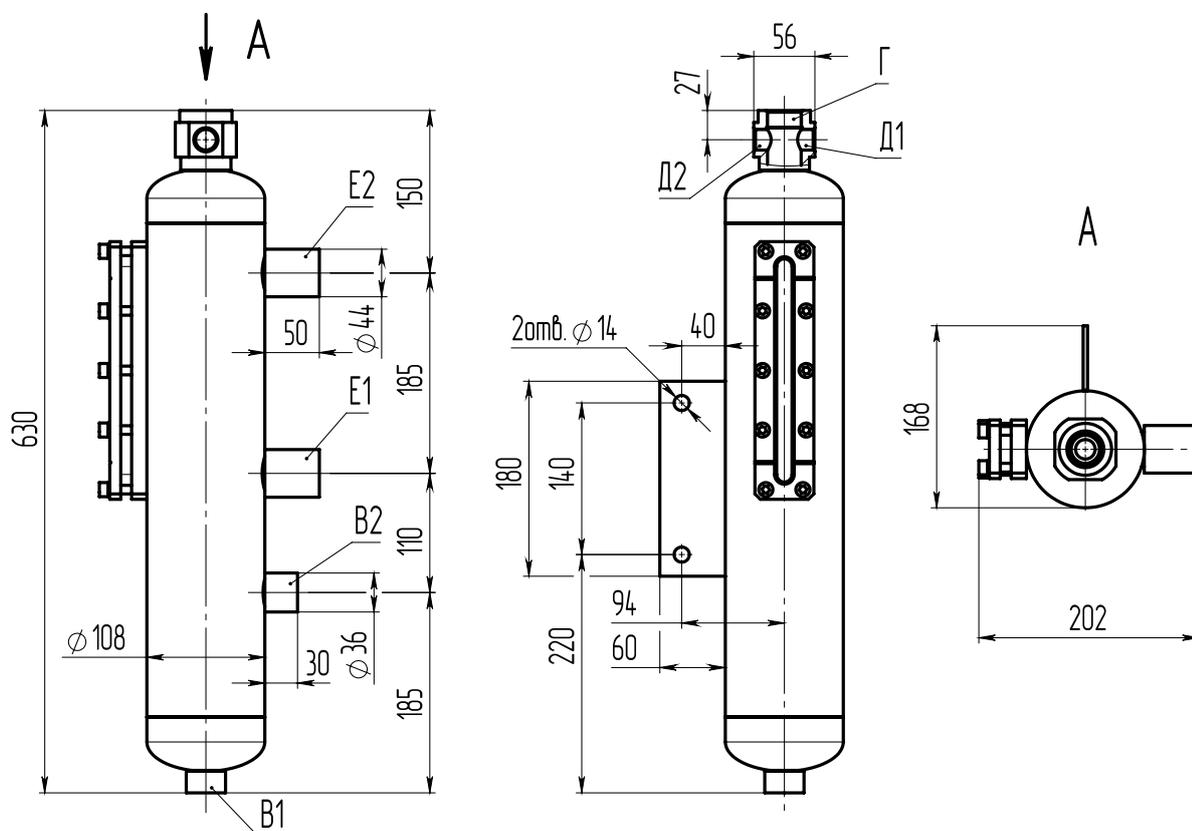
Габаритный чертеж бачка БТУ-4
